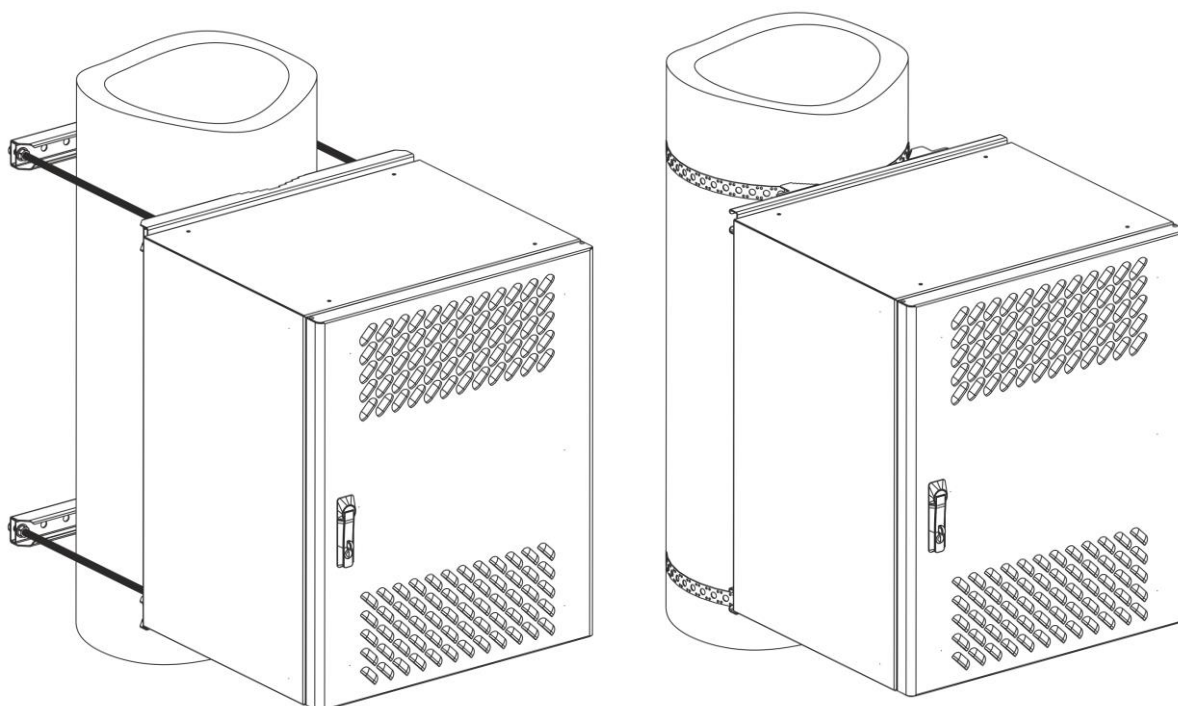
Общий вид шкафа с комплектом крепления на столб
